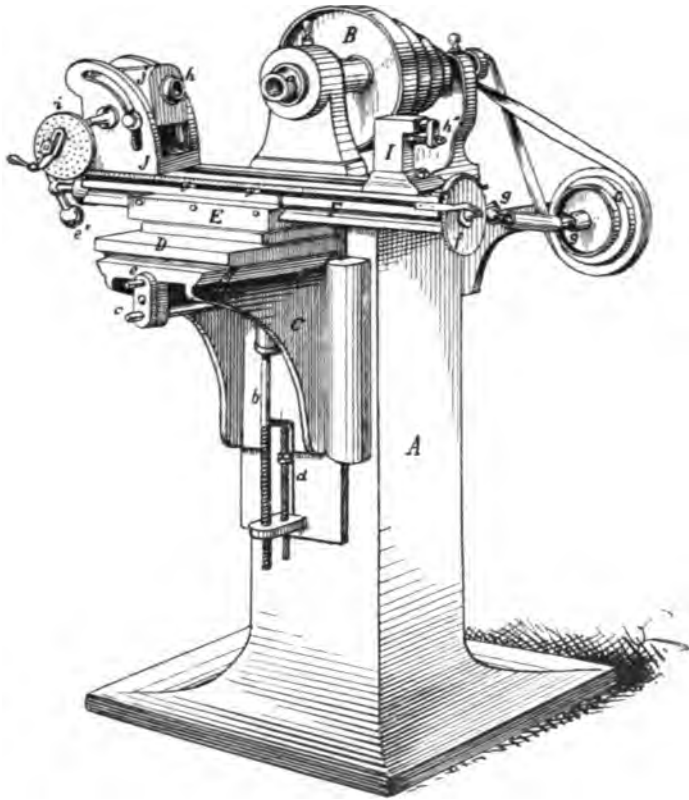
Universalfräsmaschine von Brown & Sharpe.
